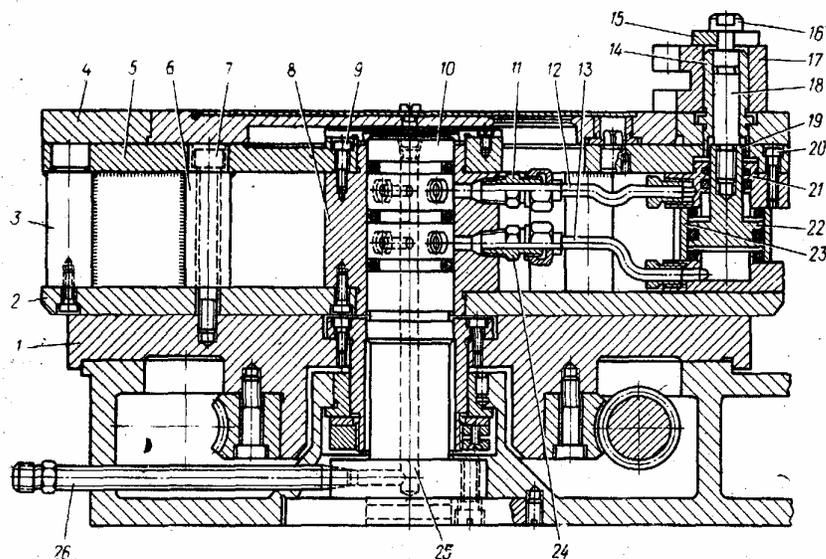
Многоместное приспособление с гидроприводом для фрезерных станков с вращающимся столом
